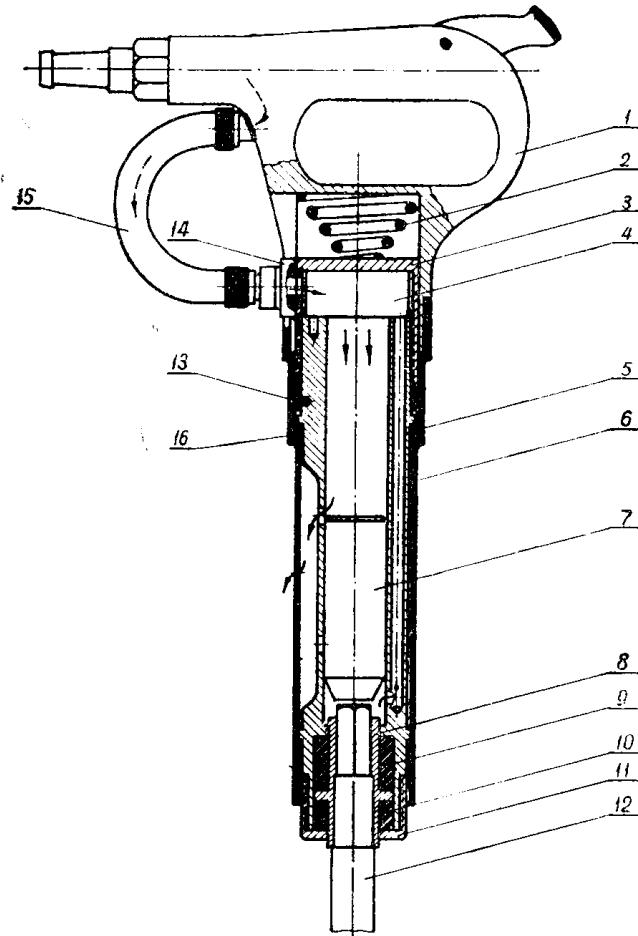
Схема ручного пневматического молотка с виброгасящими устройствами.
